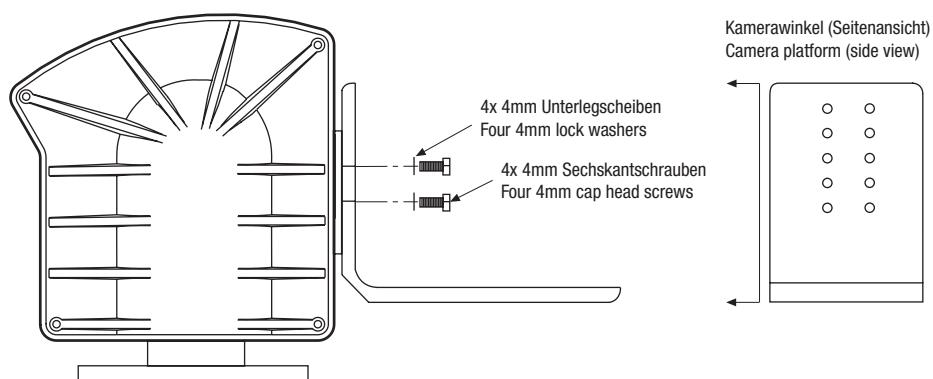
Montage des Wetterschutzgehäuses auf dem Kamerawinkel
